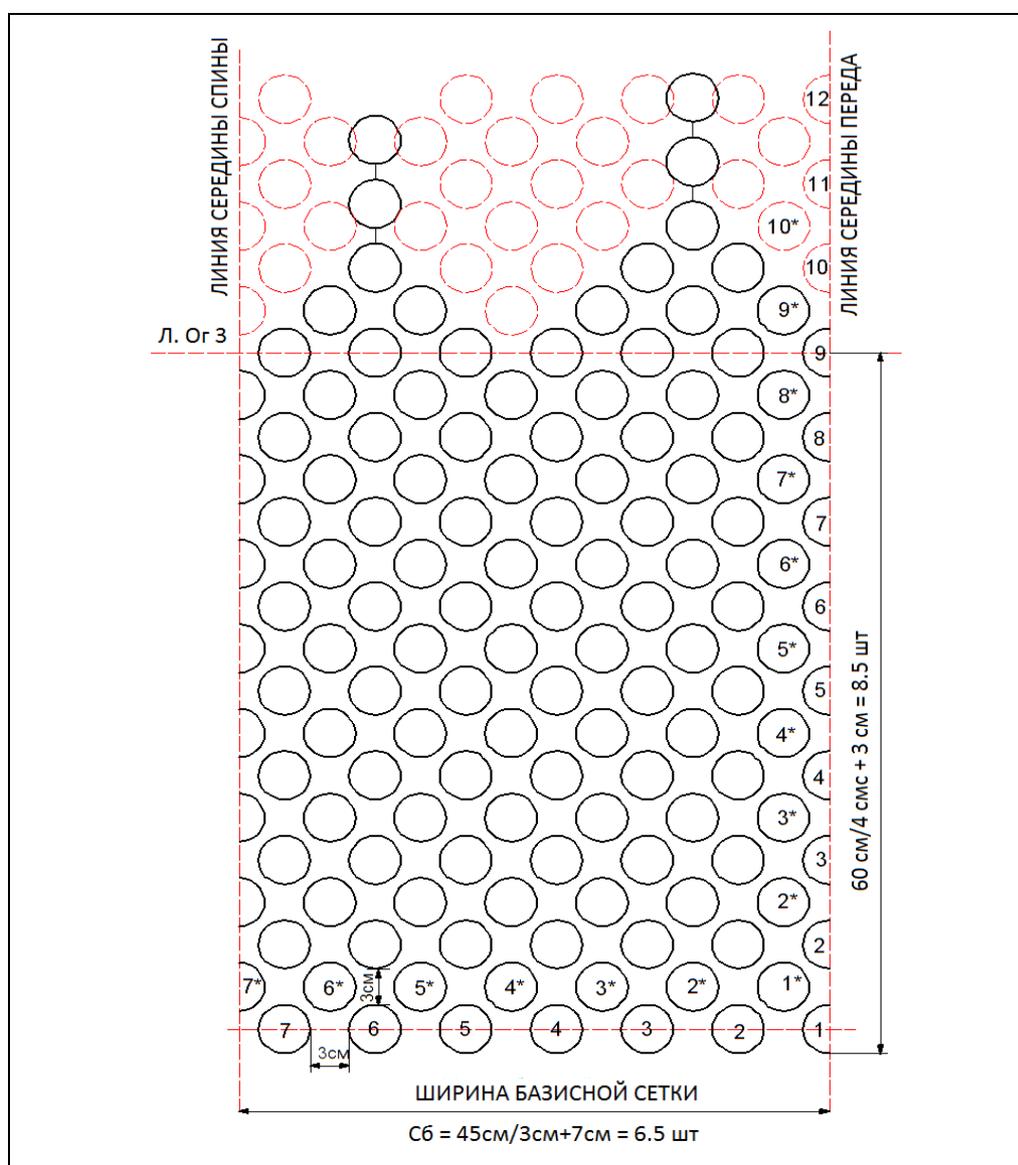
Чертеж развертки конструкции многодетального платья, состоящего из равных деталей
